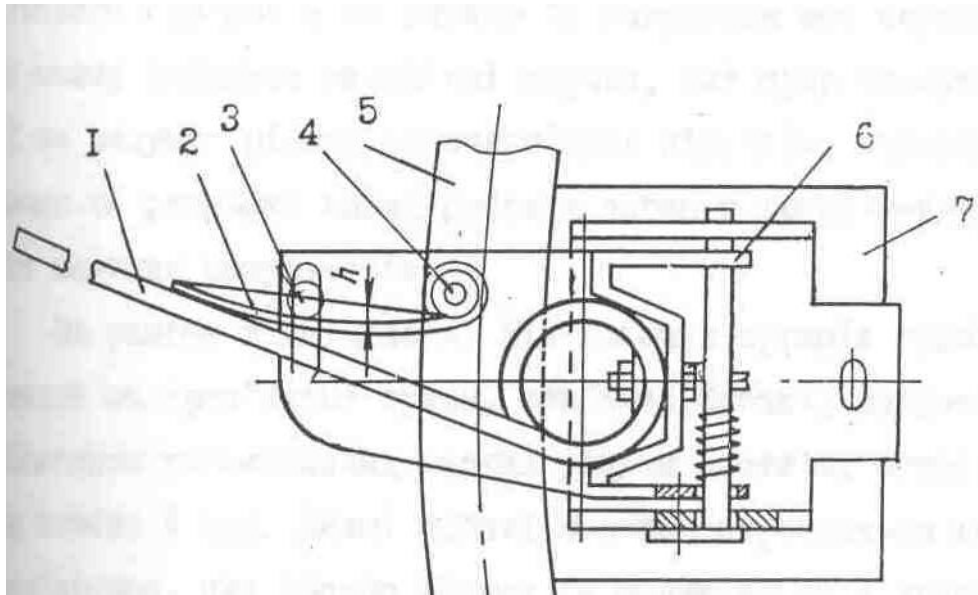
Схема удосконалення робочих органів ворушилки ВЦН-Ф-3: 1 - пружинні зуби; 2 - вітровий щит; 3 - упор; 4 - шарнір; 5 - обід ротора; 6 - поворотна обойма; 7 - кронштейн
